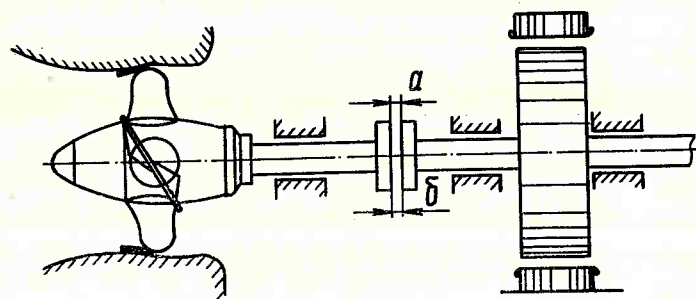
Схема центрирования трехопорного ротора горизонтального гидроагрегата (а-б), оси валов совпадают
